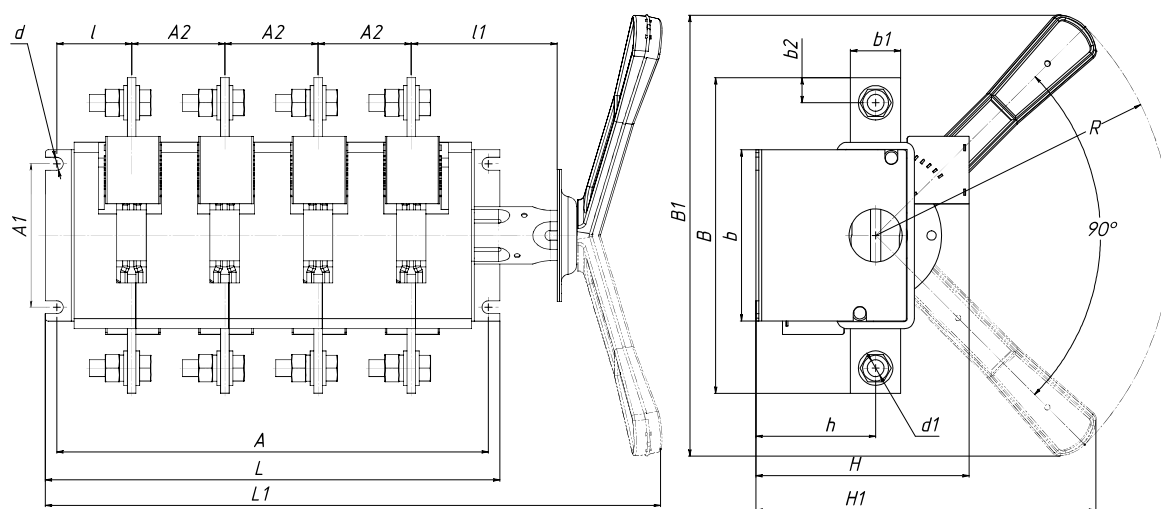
Выключатель-разъединитель на одно направление 4-полюсный с боковой смещенной ручкой
